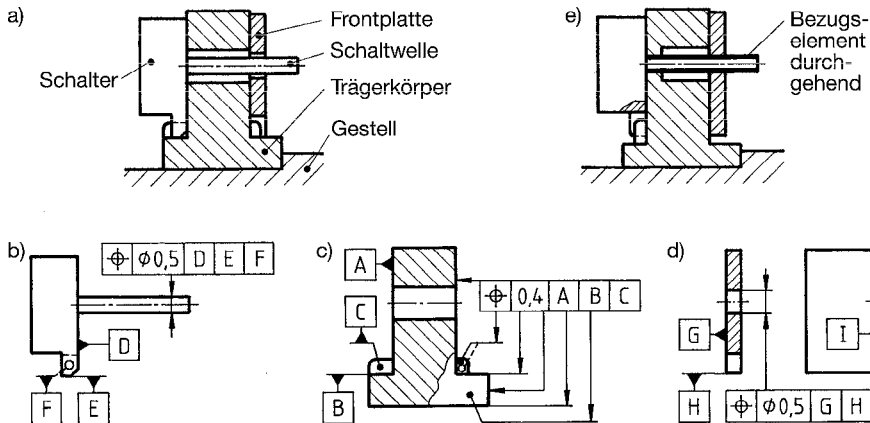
Bezugsaufbau in einer (stark vereinfachten) Baugruppe. a) Gruppenzeichnung; b) Einzelzeichnung Schalter, c) Trägerkörper, d) Frontplatte; e) toleranzgünstige Alternative mit durchgehendem Bezugselement
